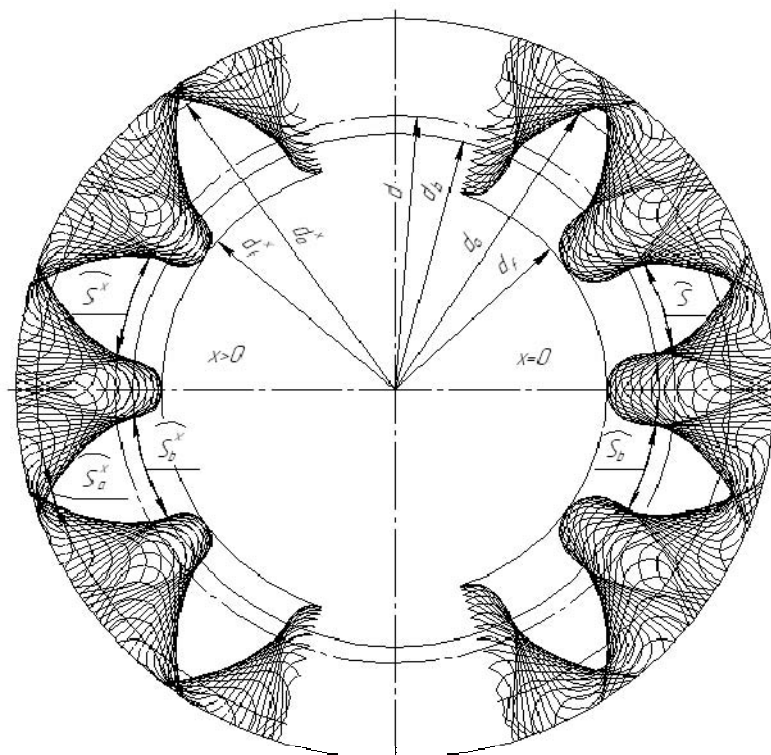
Бумажный круг с вычерченными профилями зубьев
